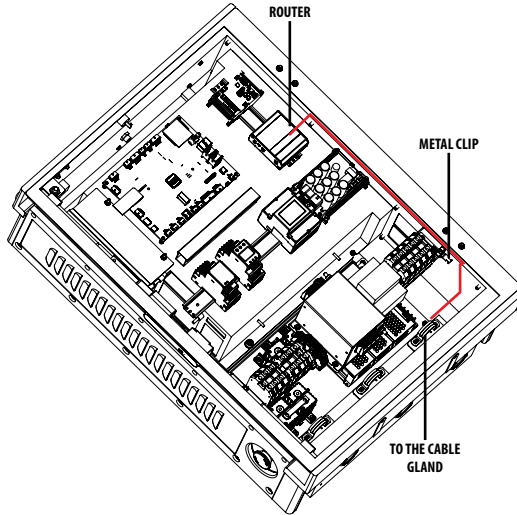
ROTEAMENTO DE CABO ETHERNET
